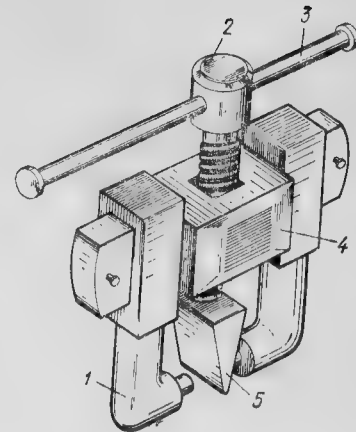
1 — крюк; 2 — винт; 3 — вороток; 4 — траверса-гайка; 5 — клин
